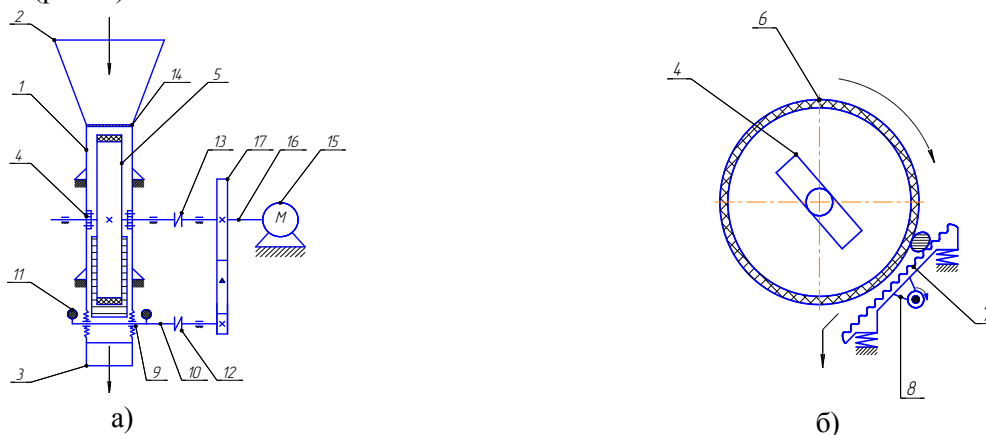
Вібраційне обладнання для лушення волоських горіхів: а) принципова схема; б) робочі органи; 1 – корпус; 2 – завантажувальний бункер; 3 – розвантажувальна горловина; 4 – варіативний механізм; 5 – дробильне колесо; 6 – гумове покриття; 7 – підпружинене рифлене деко (рис. 3); 8 – опори (рис. 3); 9 – підшипникові вузли; 10 – приводний вал; 11 – дебаланси; 12, 13 – еластичні муфти; 14 – шиберна заслінка; 15 – електродвигун; 16 – приводний вал; 17 – клинопасова передача
